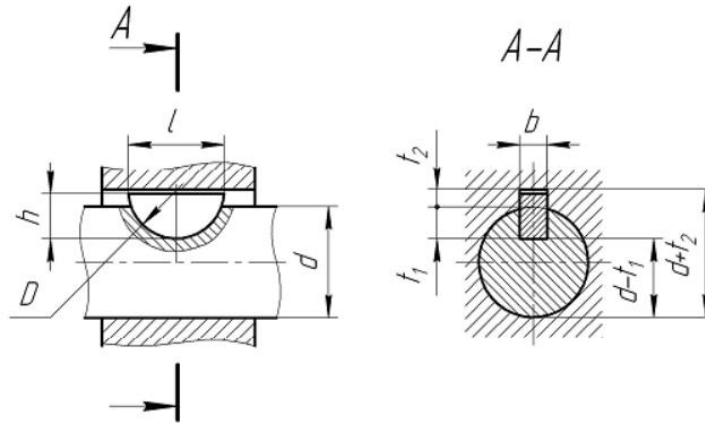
Розрахункова схема з'єднання сегментною шпонкою
